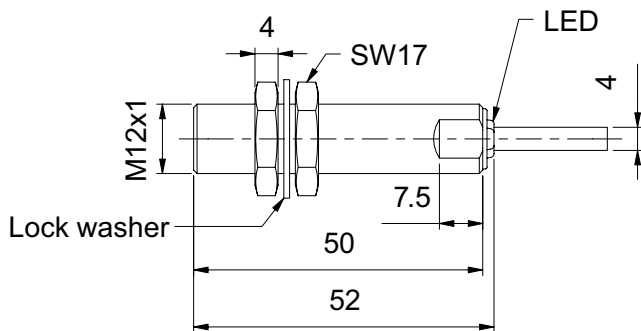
Lange Ausführung, bündiger Einbau, Kabel
